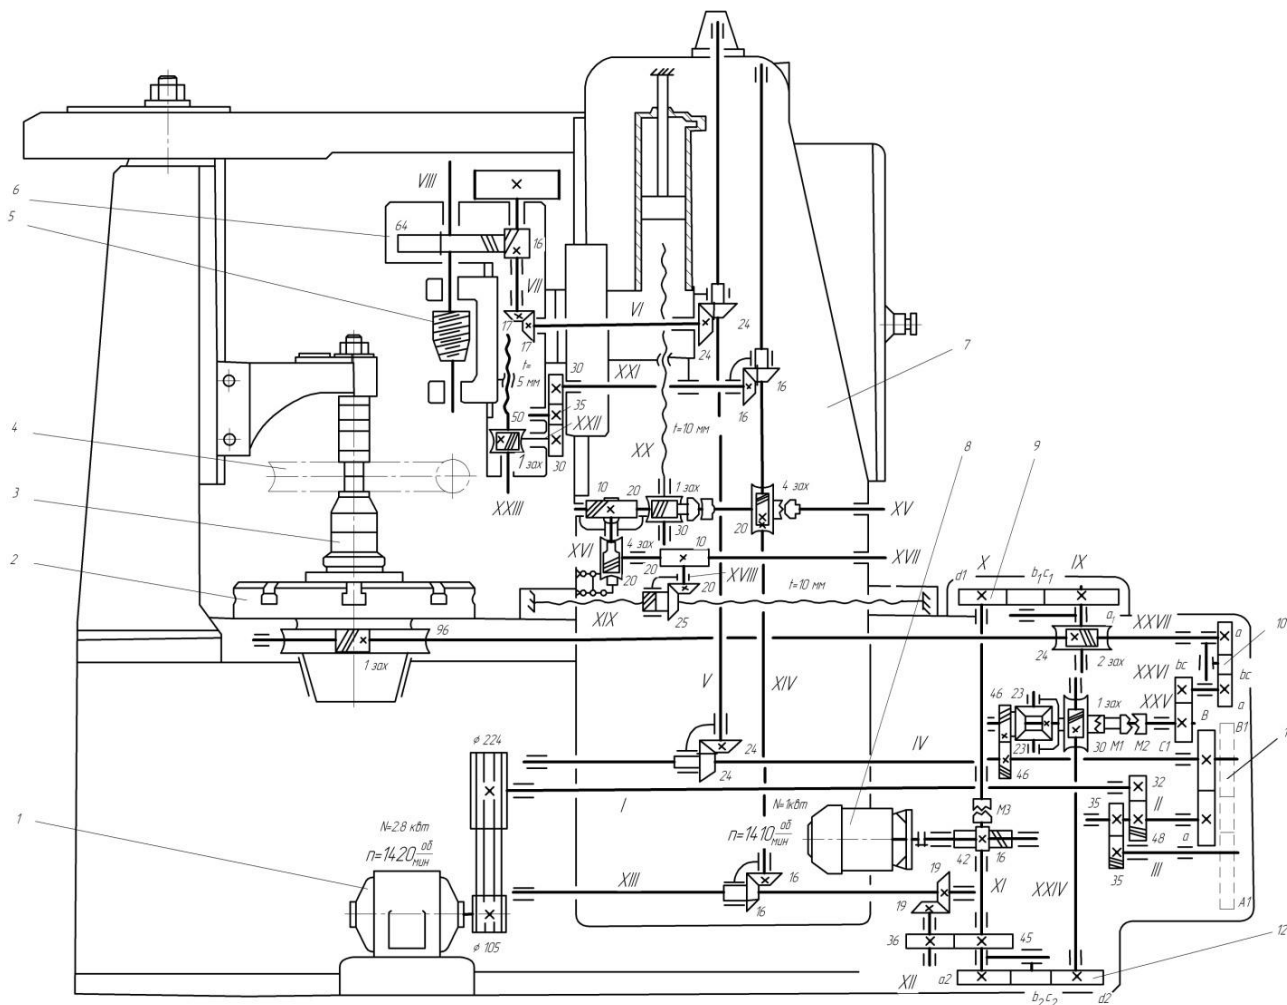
Кинематическая схема вертикально зубофрезерного станка 5Д32
